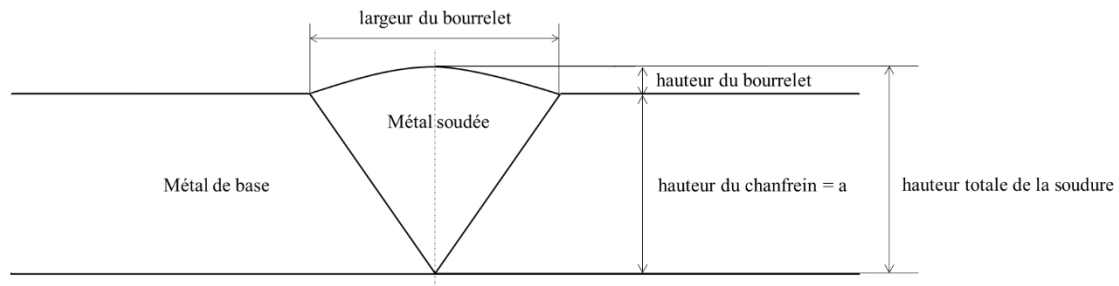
Définition de la hauteur totale de la soudure (hauteur de chanfrein + hauteur du bourrelet) et de la largeur de la dernière couche (largeur du bourrelet).
